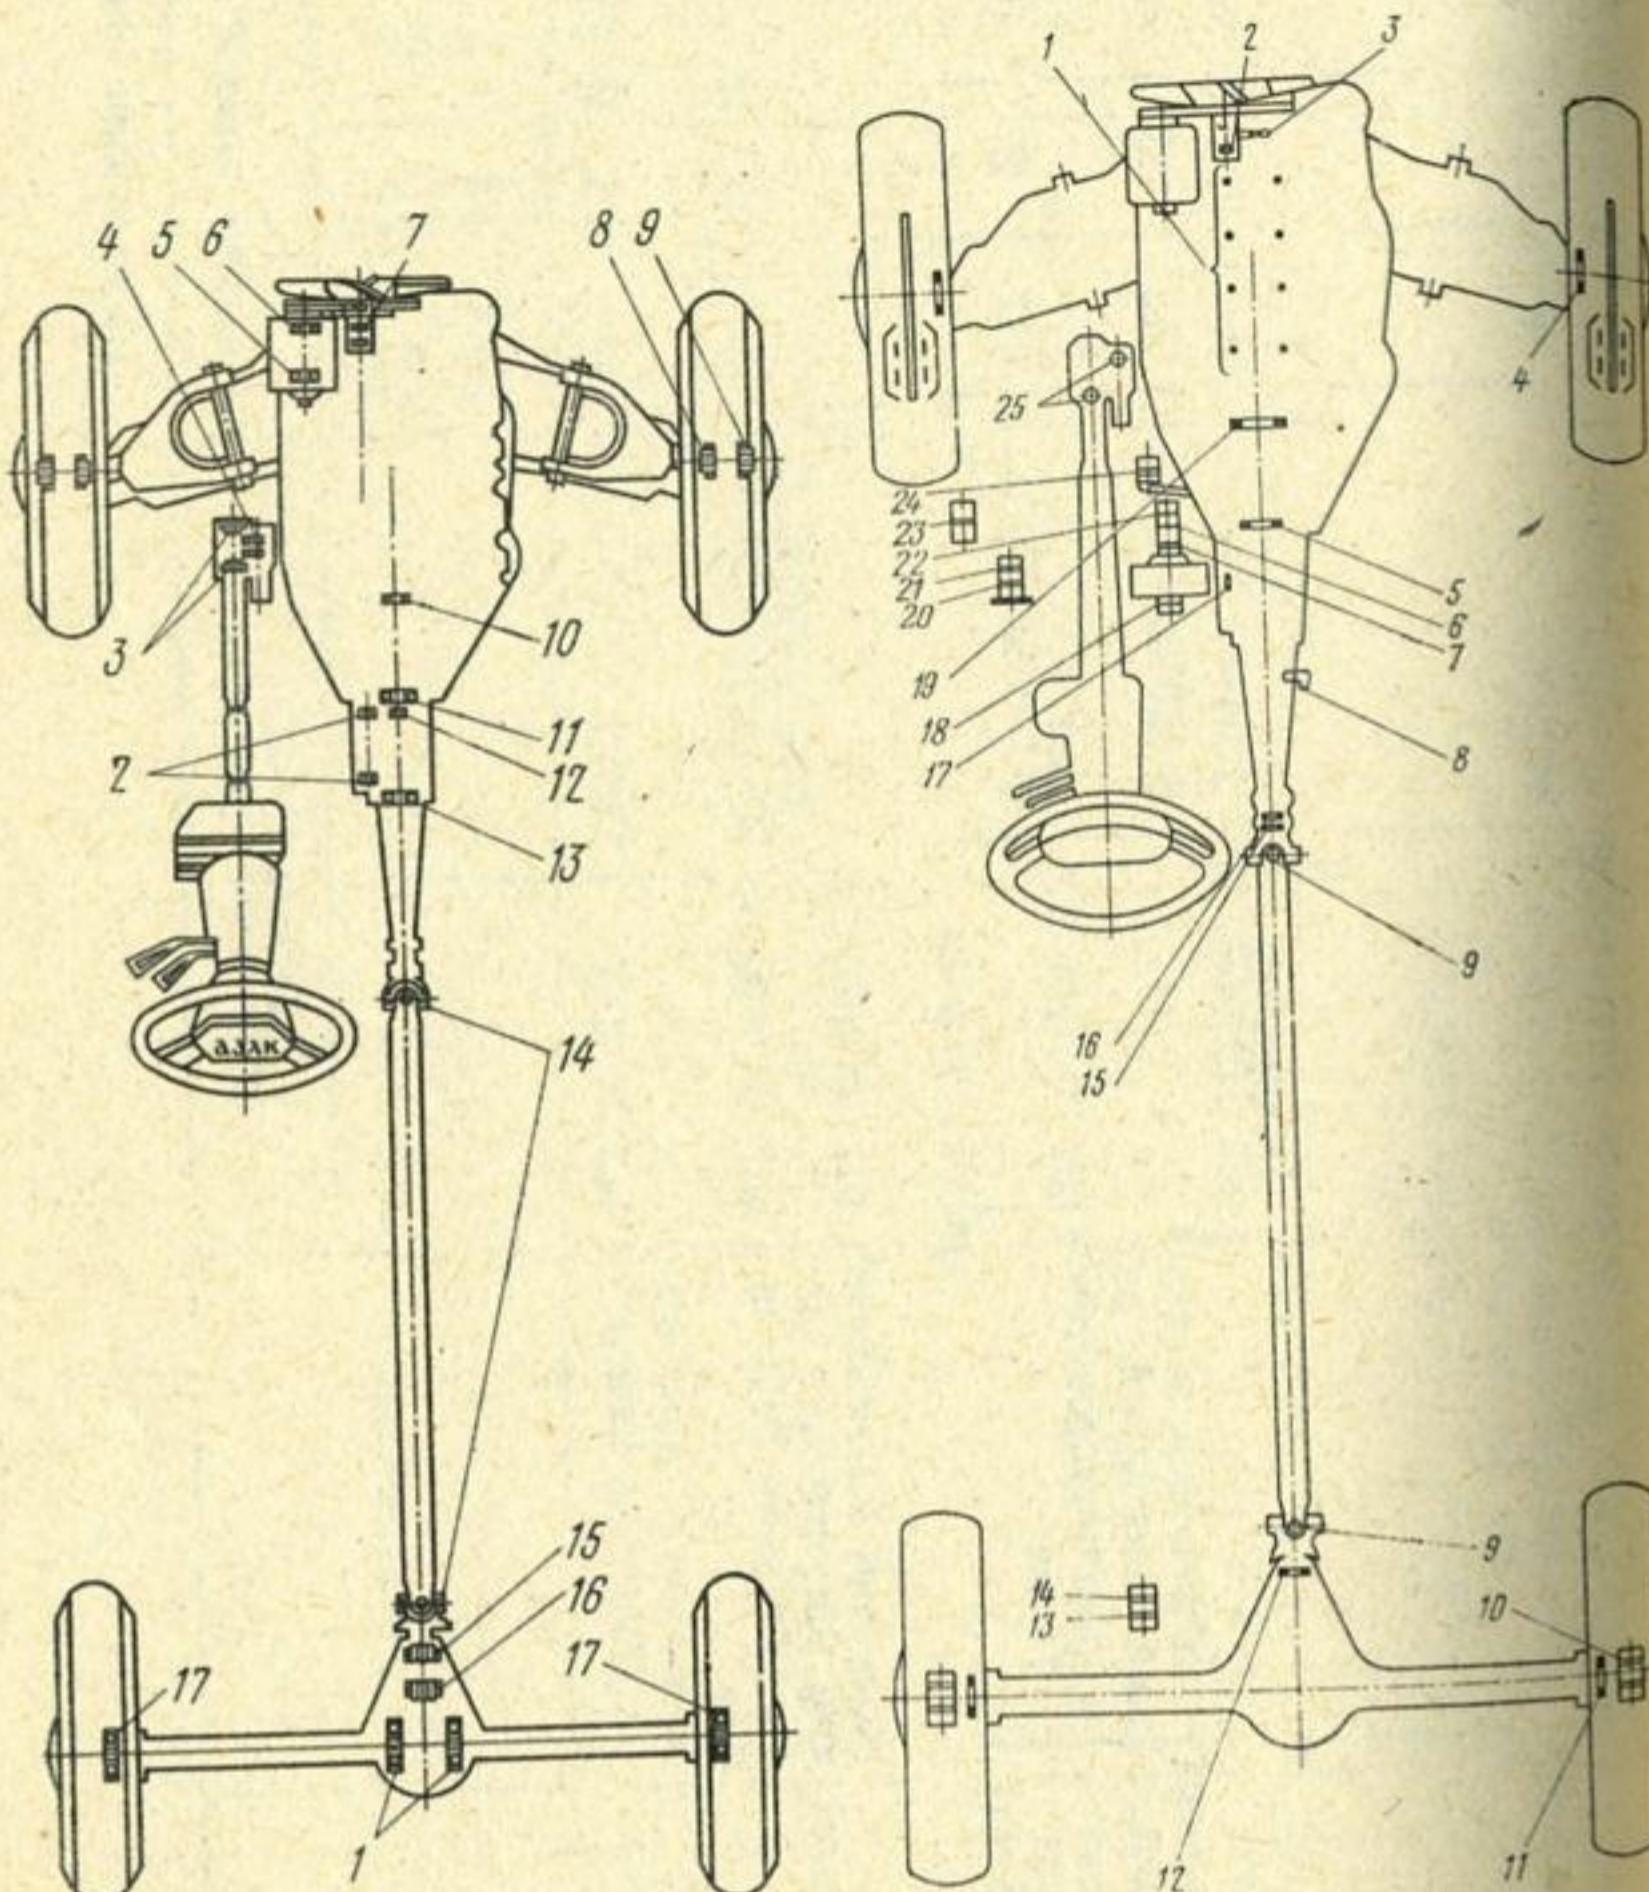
Схема расположения подшипников качения в агрегатах, механизмах и узлах автомобиля (обозначение позиций см. в табл. 2 приложения)
